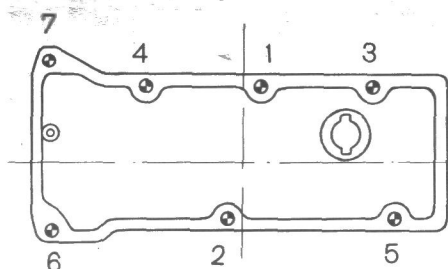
Порядок затягивания гаек крепления крышки головки цилиндров двигателя ВАЗ-2105
